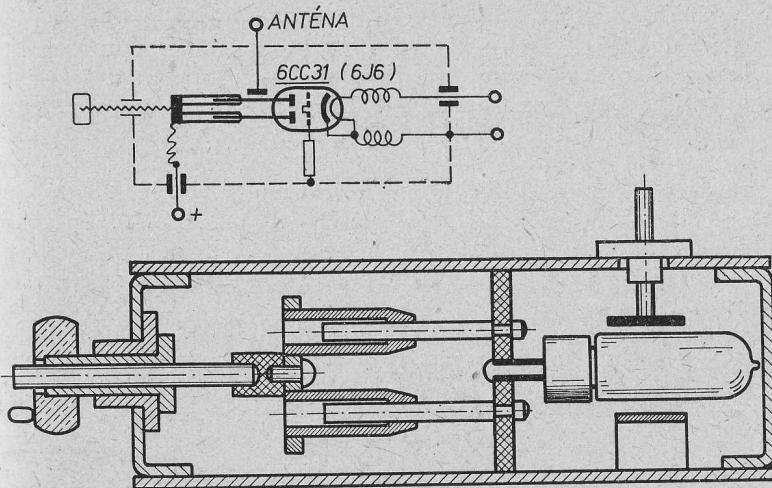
Oscilátor s tyčovými obvody a tužkovými elektronkami.
